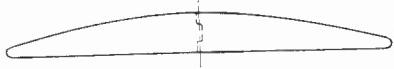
Metallluftschraube aus Aluminiumblech getrieben.
